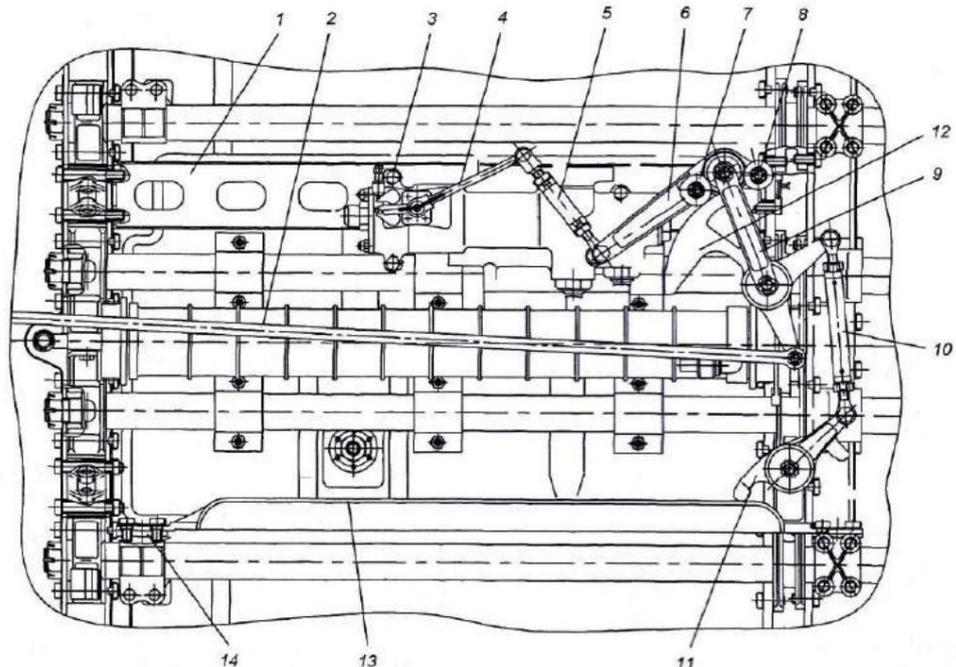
Механизм управления и блокировки РУ двигателя ПС-90А
